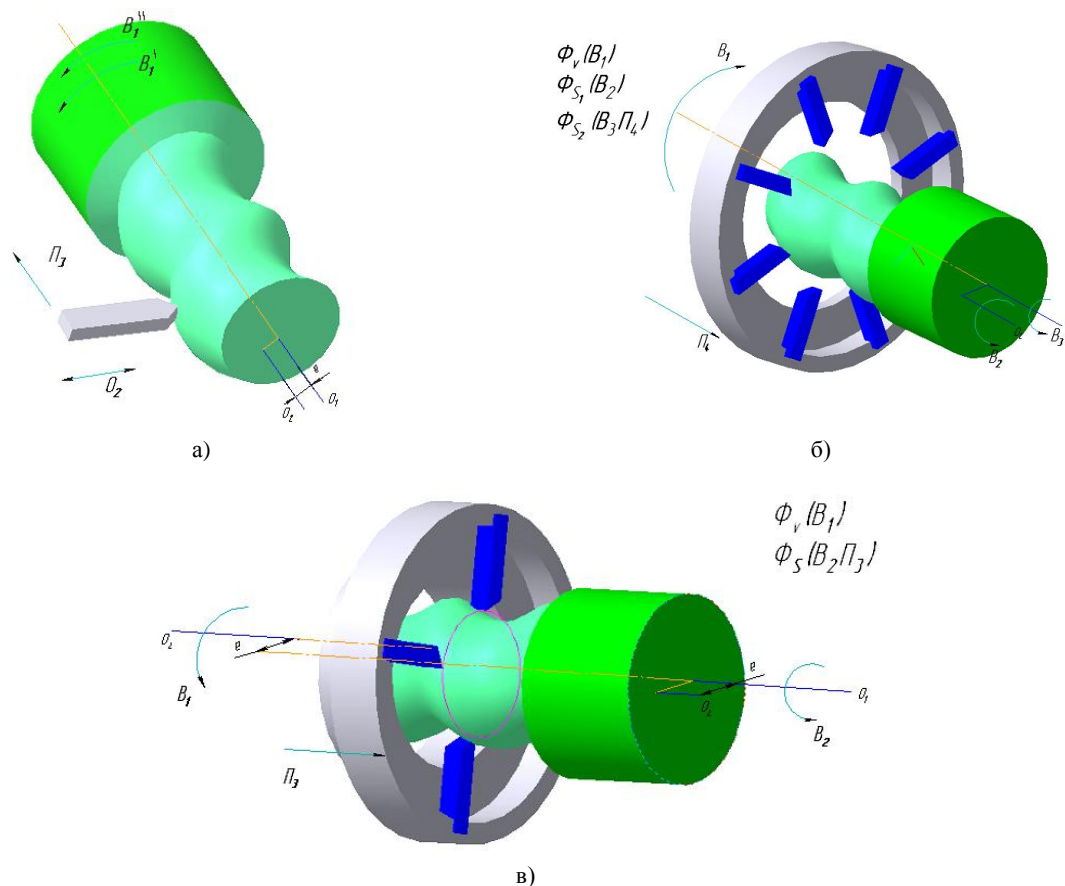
Кинематические схемы обработки круговых винтовых поверхностей
